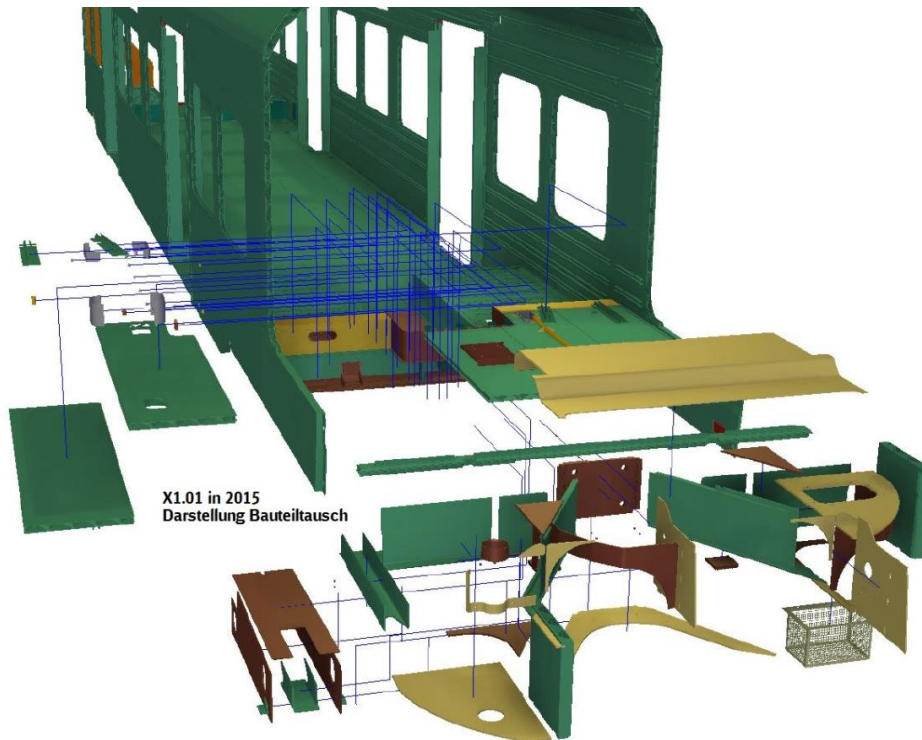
Explosionsansicht der Reparaturbaugruppen, Bildrechte: DB Systemtechnik, M. Bretschneider
